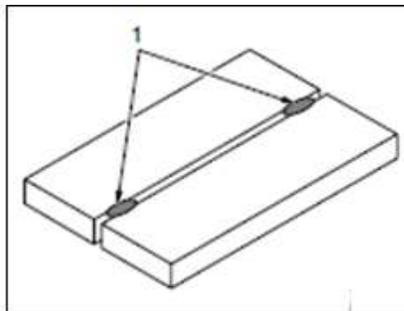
Figura de dos placas soldadas a tope con dos puntos de soldadura
